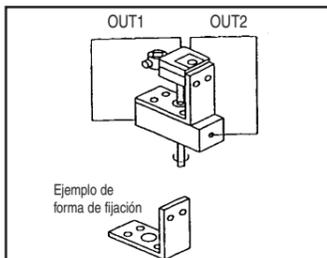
Ejemplo de montaje mediante el tornillo lateral del posicionador
